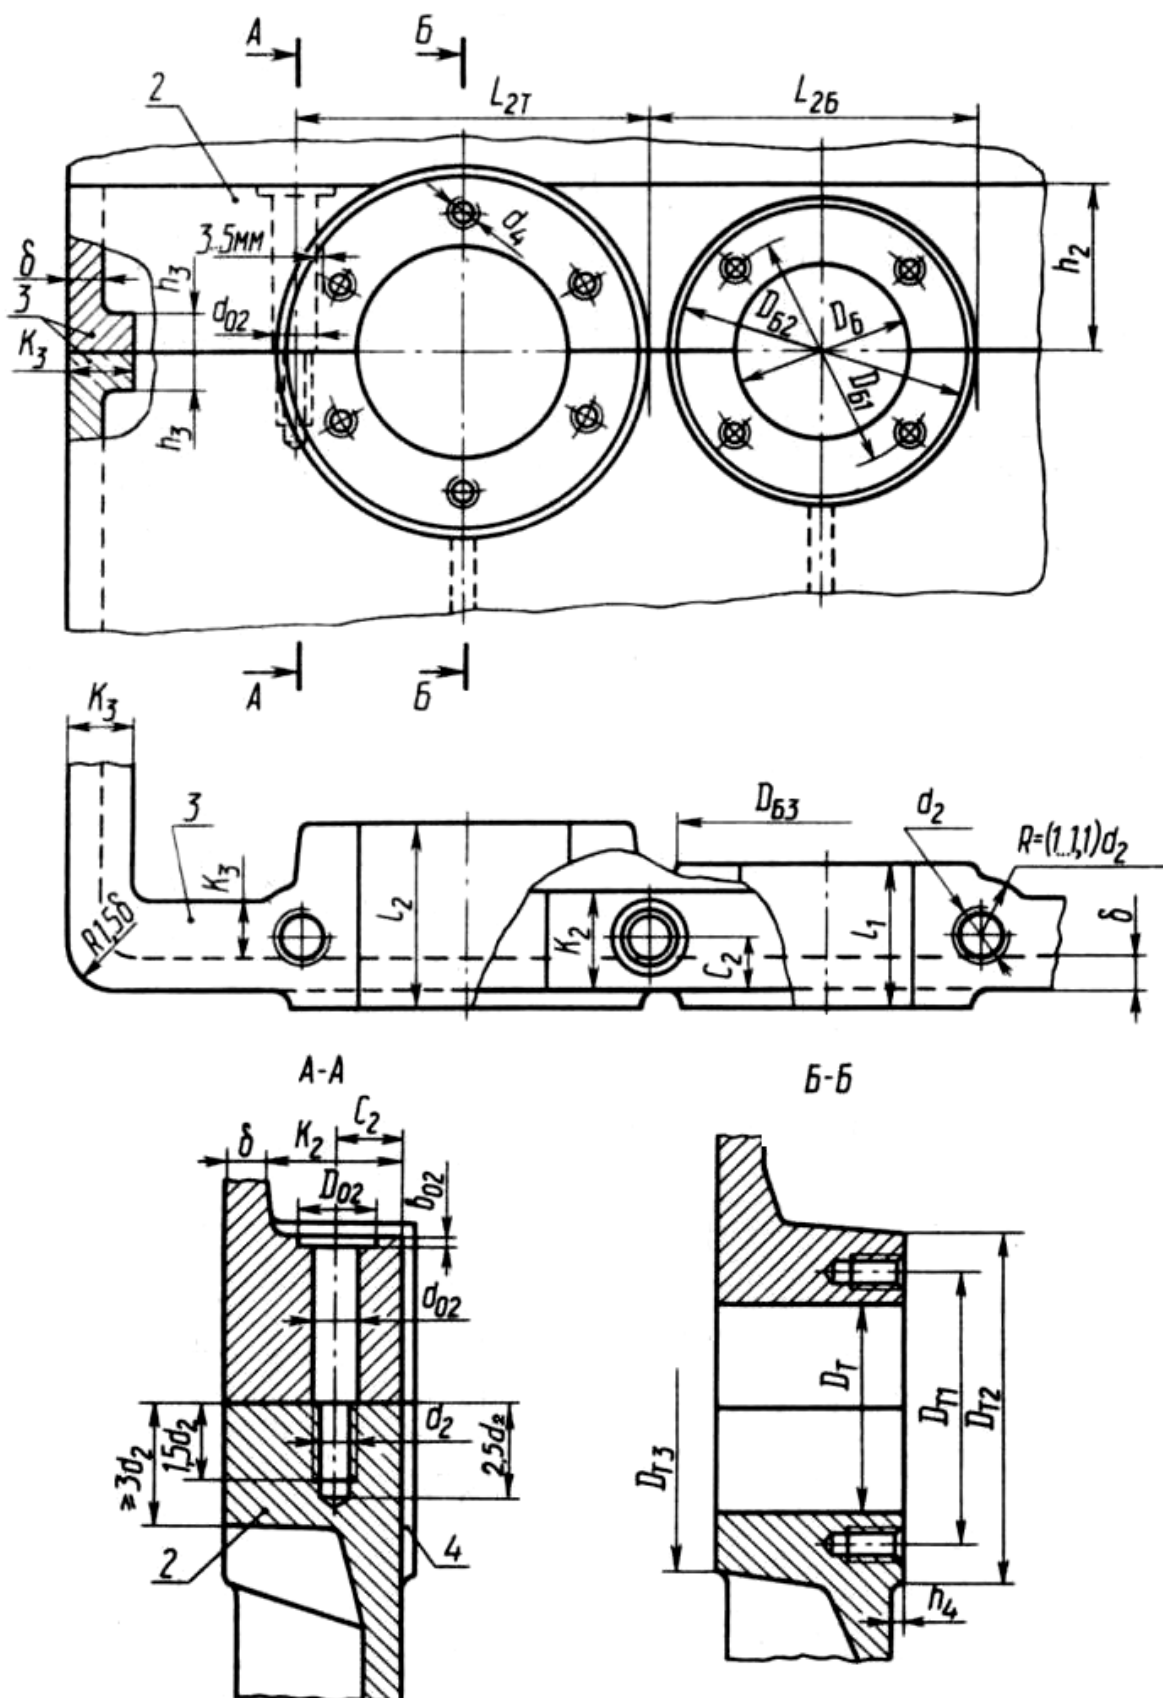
Подшипниковые бобышки с отверстиями для болтов под накладные крышки
